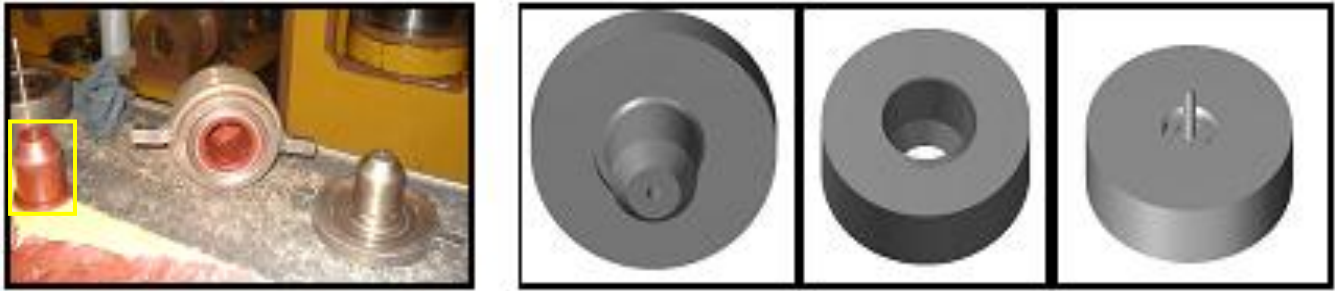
Molde actual (izquierda) y molde mejorado (derecha) del empaque tulipa
